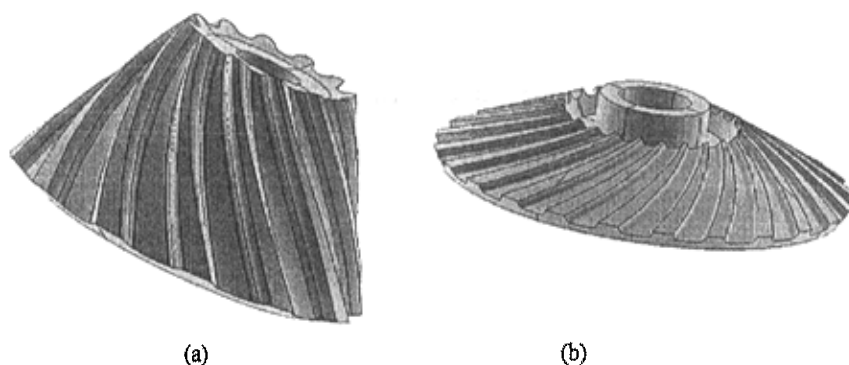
斜航式法向圆弧螺旋锥齿轮实体模型
